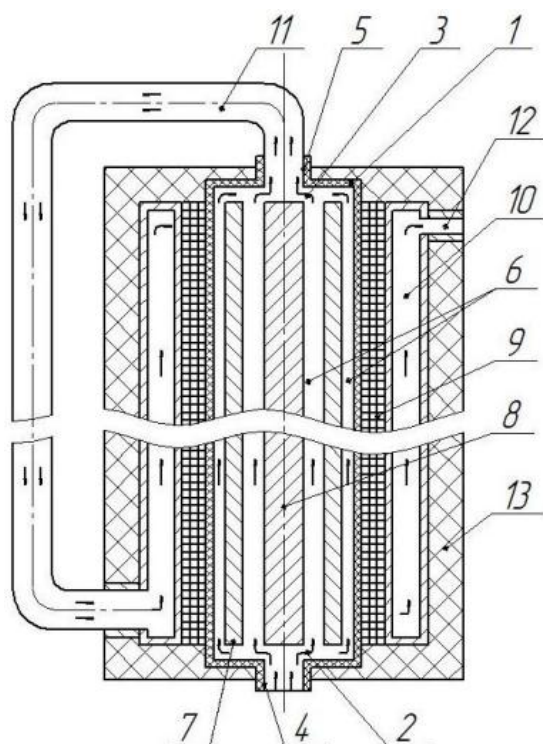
Индукционный нагреватель с выдерживателем: 1 – корпус; 2 – нижняя входная камера; 3 – верхняя входная камера; 4-5 – входные и выходные патрубки соответственно; 6 – кольцевой зазор; 7 – труба; 8 – стержень; 9 – обмотка индуктора; 10 – выдерживатель; 11 – обводная труба; 12 – выходной патрубок; 13 – теплоизоляционный слой.
